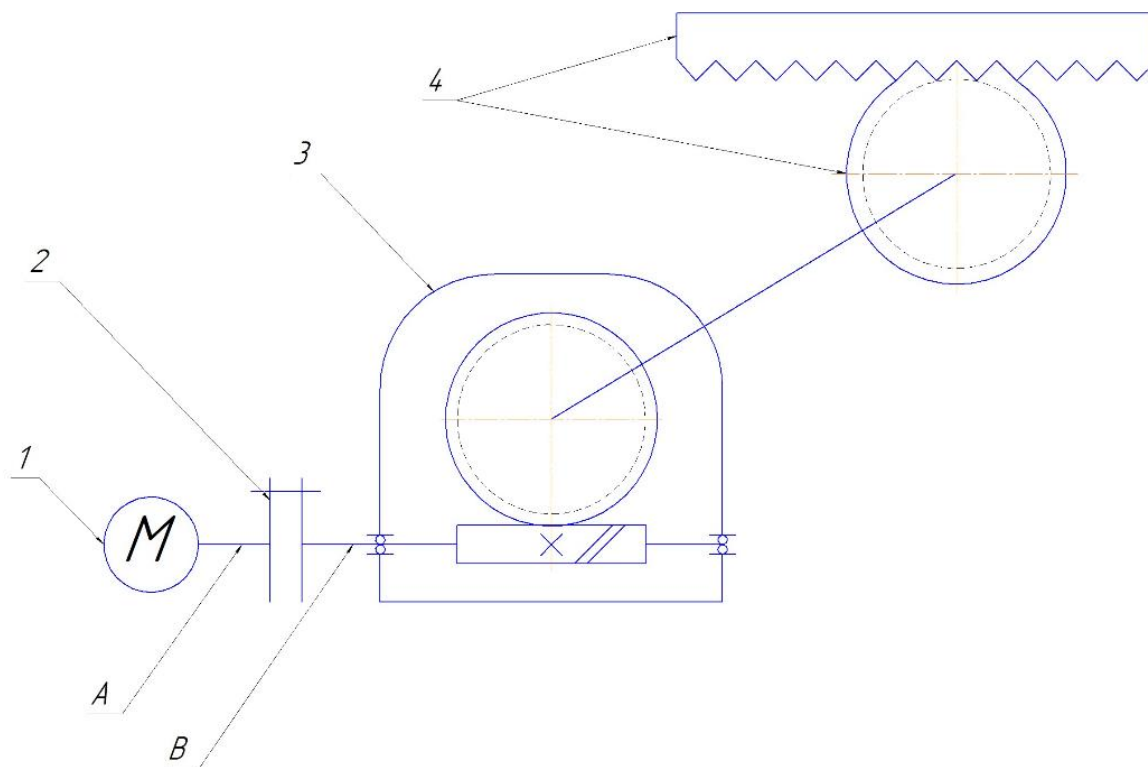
Кинематическая схема привода трехзвенного робота-манипулятора по оси «X» («Y»; «Z»)
